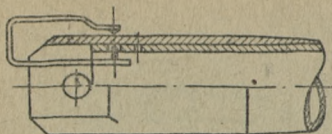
Кернер для разметки отверстий на стыковочном стакане
